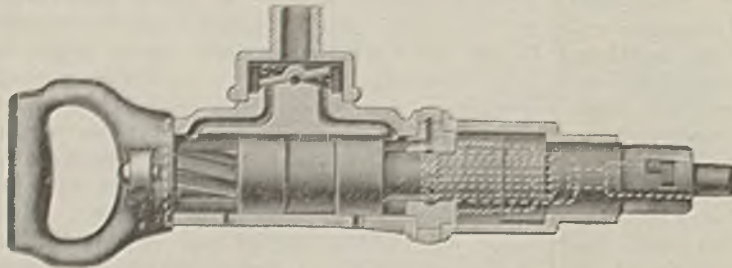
Längsschnitt der Westfalia-Bohrmaschine.
